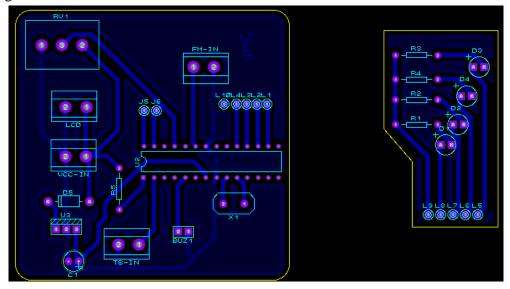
Diseño PCB de sistema integral para detección de fallas e indicador visual
